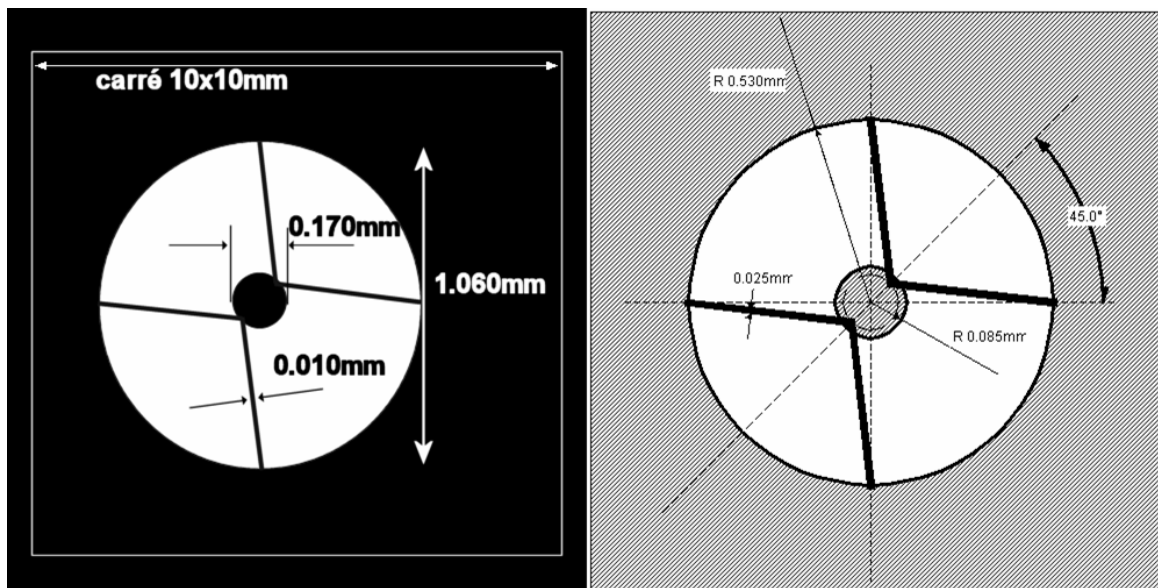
Dimensions et angles pour la fabrication du Lyot stop.
